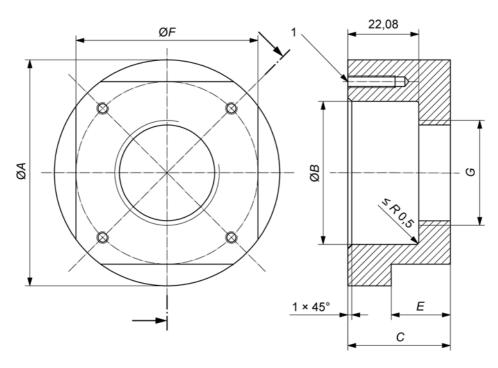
Крышка генератора возмущений с резьбовым соединением, с размерами, приведенными в таблице В.1
